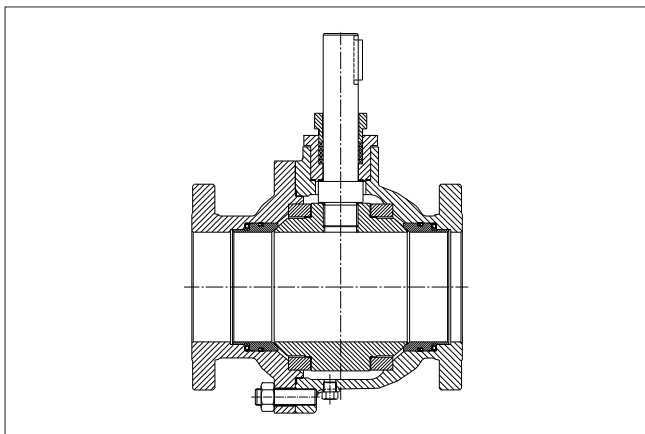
Construction à tourillon, tailles DN 600/24» et DN 400/16»
